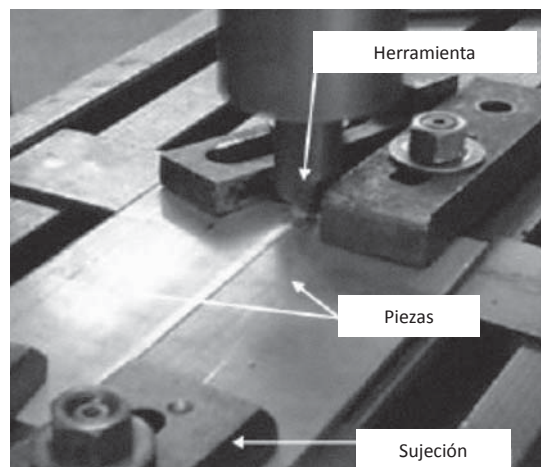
Esquema del montaje utilizado en el proceso de soldadura SFA.
